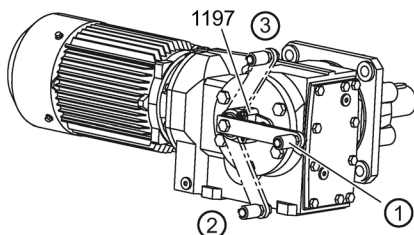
Положение рычага сцепления у типа редуктора BH. 29 - 39
